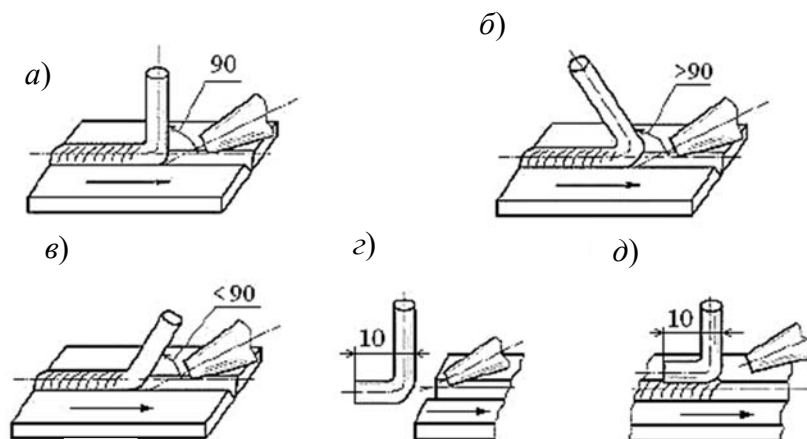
Положение присадочного прутка и горелки при сварке
